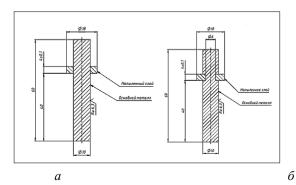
Образцы для испытаний на: a — адгезионную прочность, b — когезионную прочность
